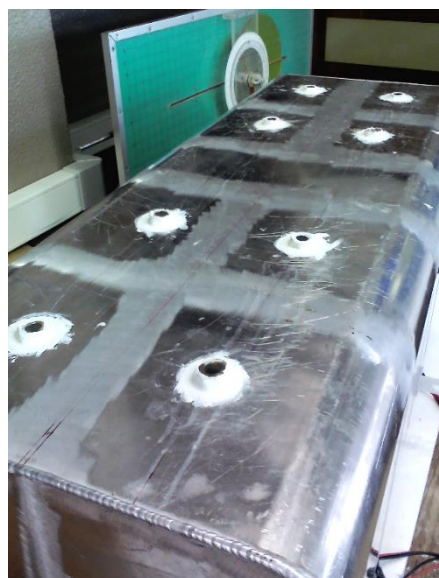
Fixação das eletroválvulas, pormenor e vista geral
